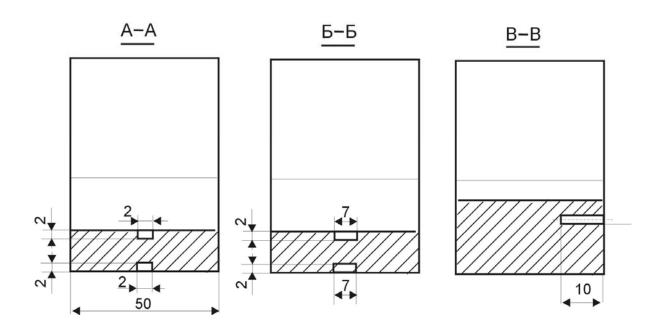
СОП для настройки ультразвукового дефектоскопа с совмещенным (С) пьезопреобразователем при контроле угловых сварных швов
